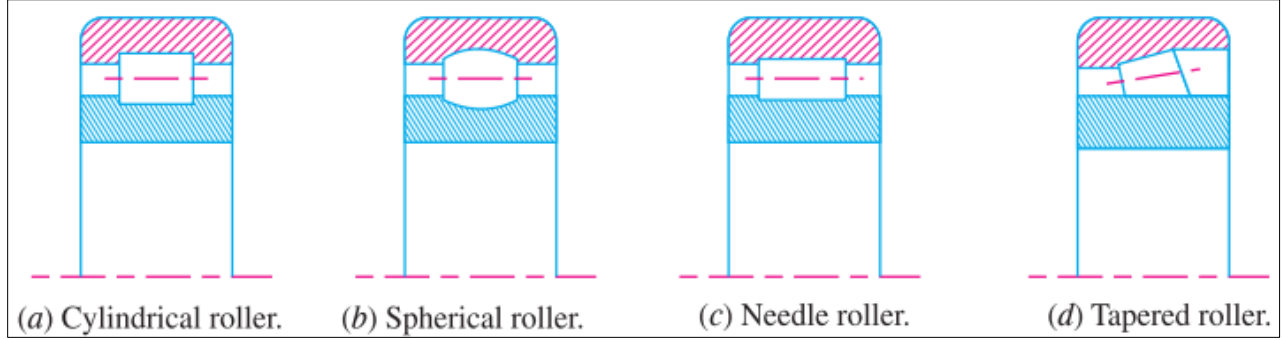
रोलर बेअरिंग्सचे प्रकार (Types of Roller Bearings)
